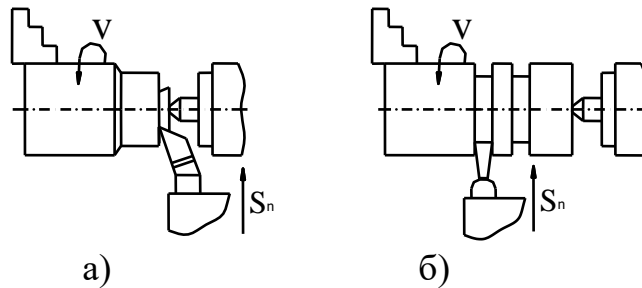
Схеми обробок торцевих поверхнь
